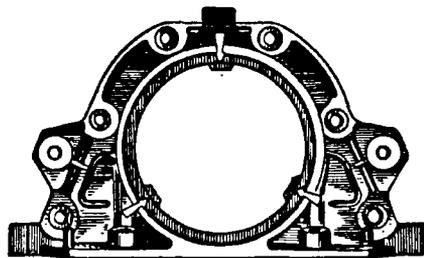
Держатель заднего сальника коленчатого вала. Стрелками указаны выступы для центрирования держателя относительно фланца коленчатого вала
